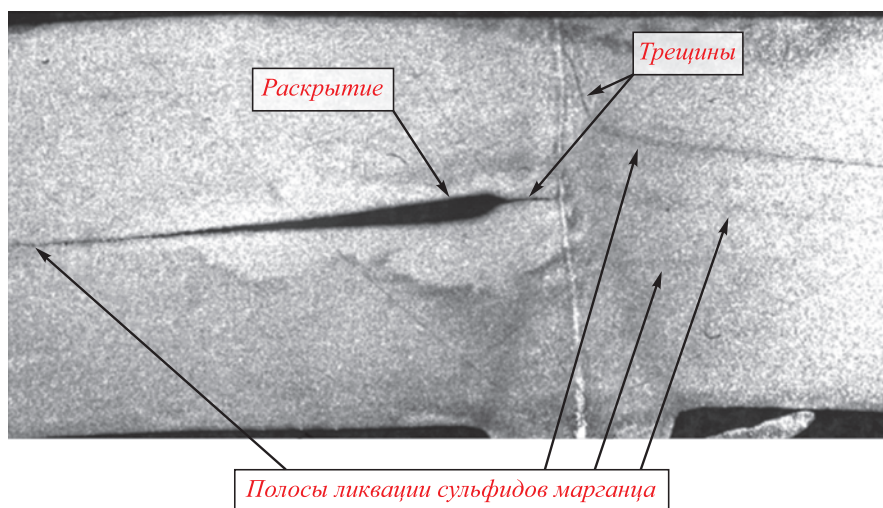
Дефекты при высокочастотной стыковой сварке труб
